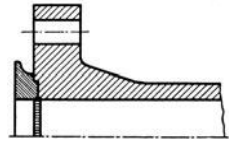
Stahlgußflansch mit eingesetztem Ansatz und Schweißlippe.
